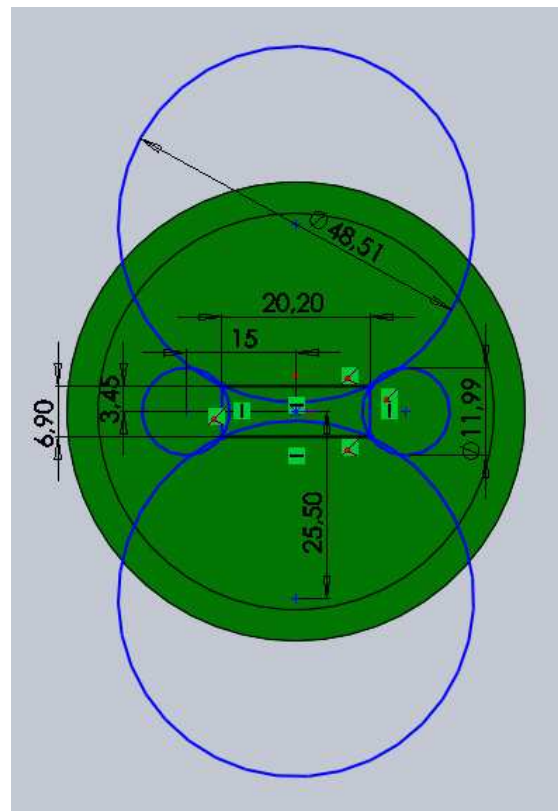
Croquis Frontal cámara de descarga molde rectangular
